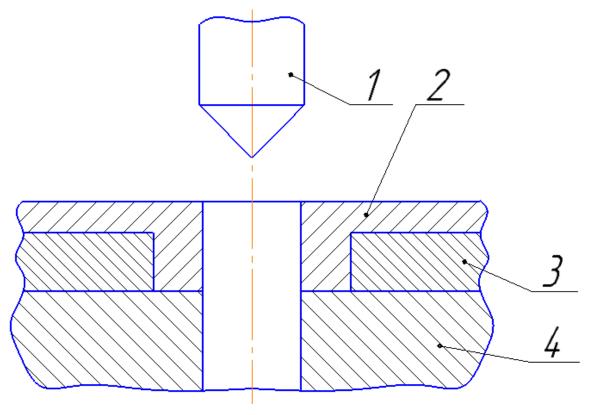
Получение отверстия с отбортовкой[10]: 1 — пуансон; 2 — тонколистовая заготовка; 3 — формообразующая матрица; 4 — обрезная матрица
